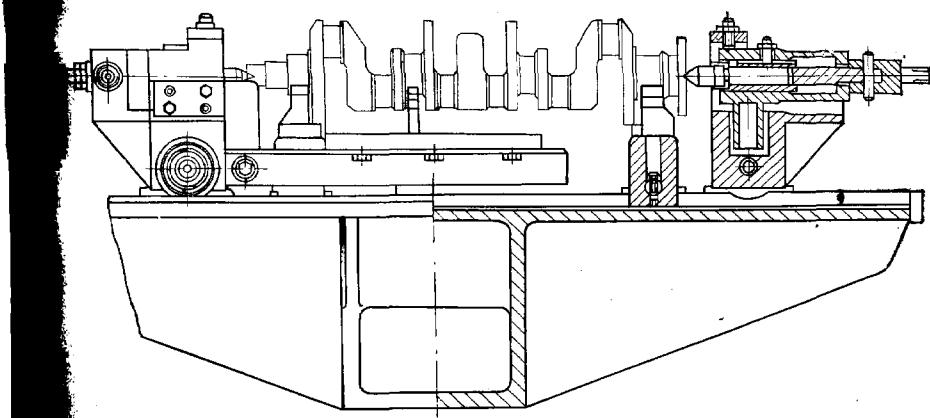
Приспособление для правки коленчатых валов, применяемое Горьковским автомобильным заводом
